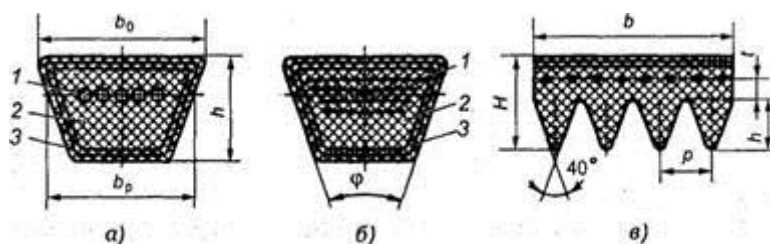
Конструкции клиновых ремней: *a* — кордшнуровой; *б* — кордтканевый; *в* — поликлиновой
